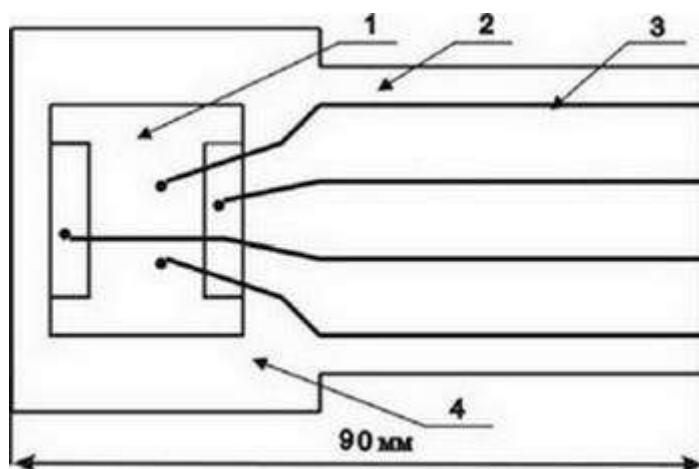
Конструкция пленочного арсенид-галлиевого датчика Холла:
